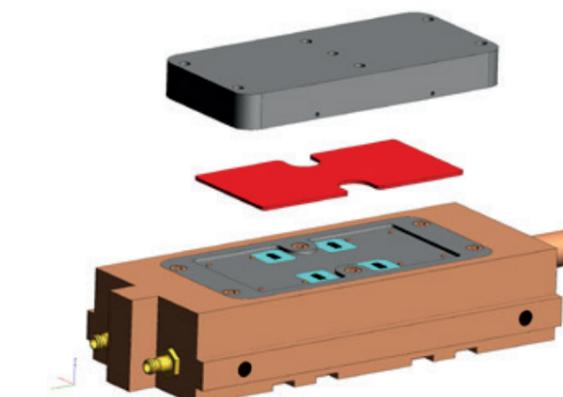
Werkzeugeinsatz mit vier Aufnahmen (blau)
